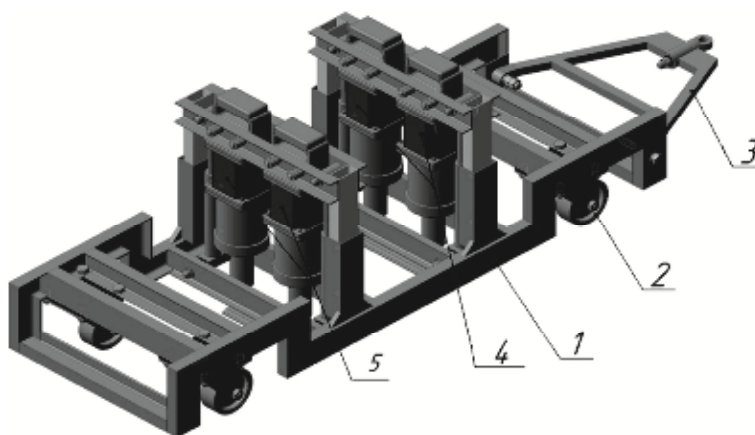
Прицепное устройство для установки резиновых шумовых полос:
